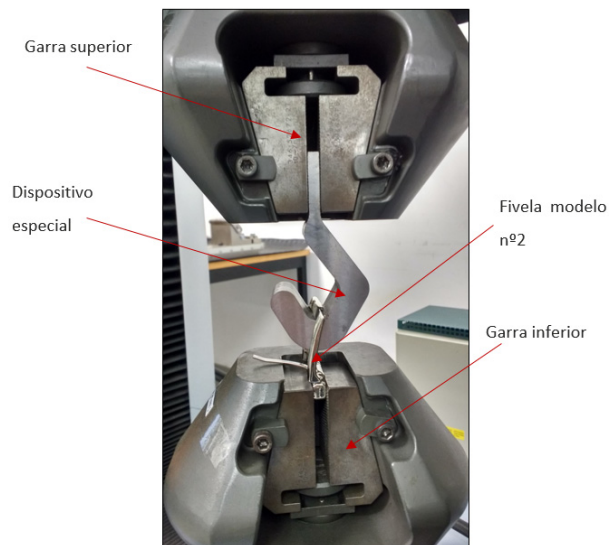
Montagem dos componentes necessários para a execução dos ensaios de tração.
